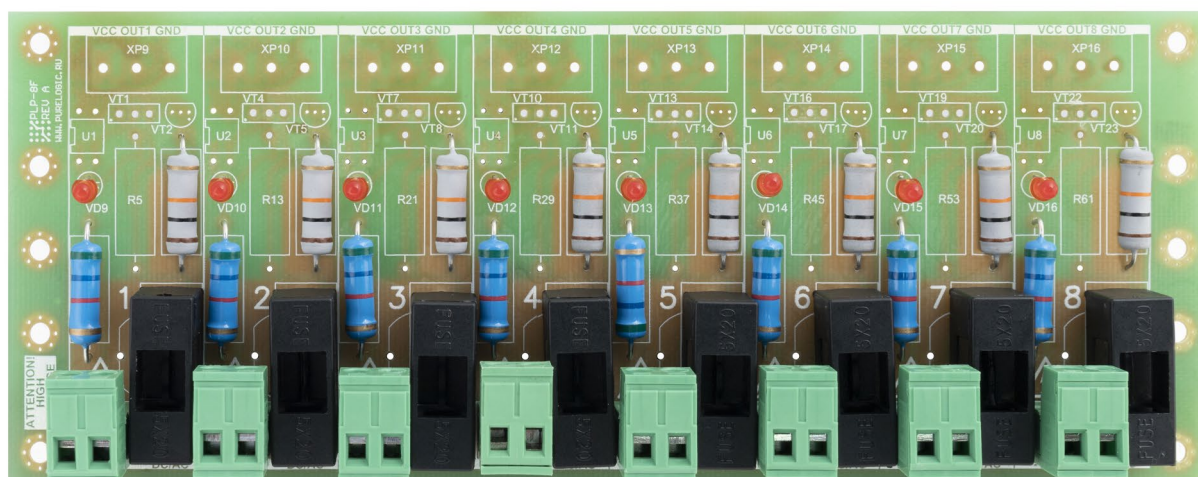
Внешний вид изделия PLP-8F-AC.
